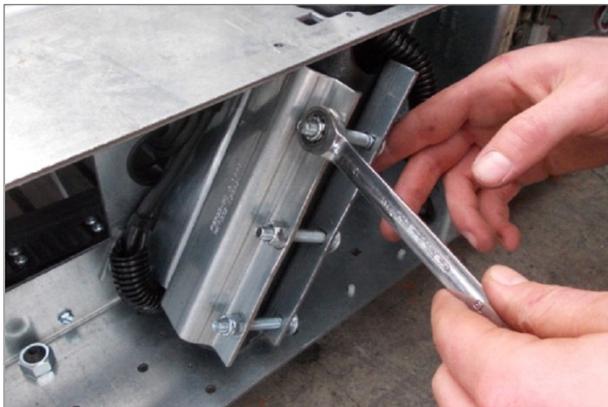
Montage Mercury/Path, Geländerbefestigung
